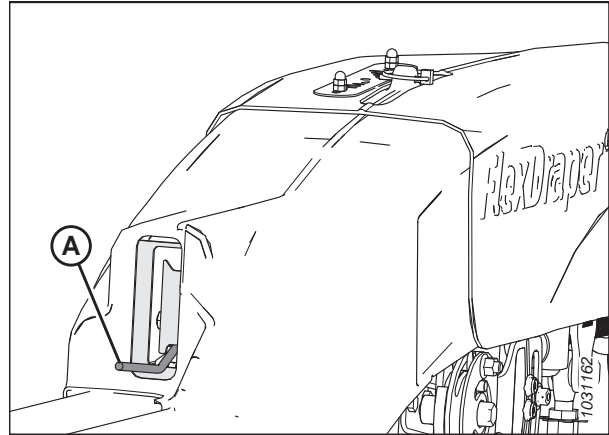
Dispositivo di bloccaggio flottazione – in posizione bloccata
